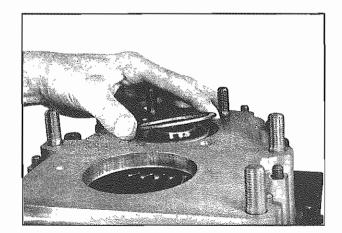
Montaggio di un rasamento di spessore Placing the one shim washer
